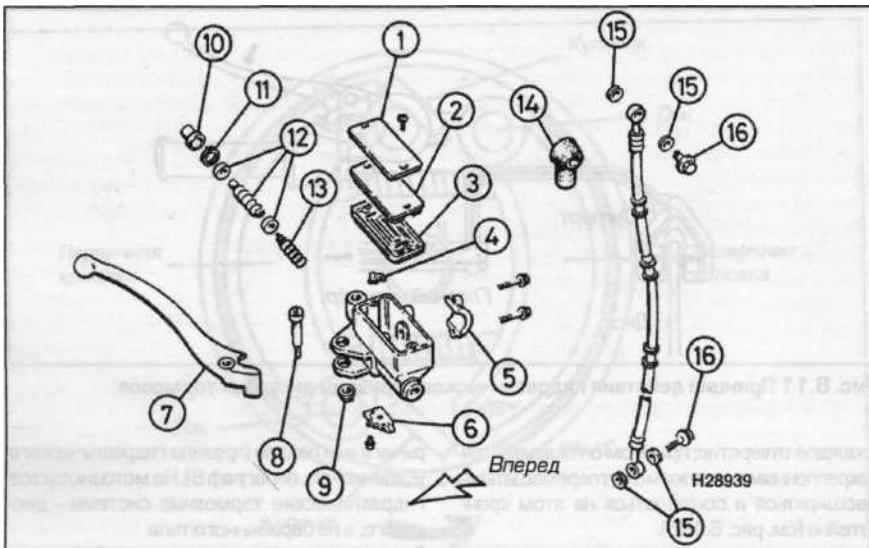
а Конструкция типичного главного цилиндра переднего тормоза
